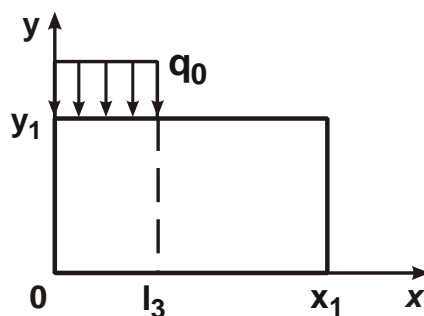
Розрахункова схема ріжучої пластини
